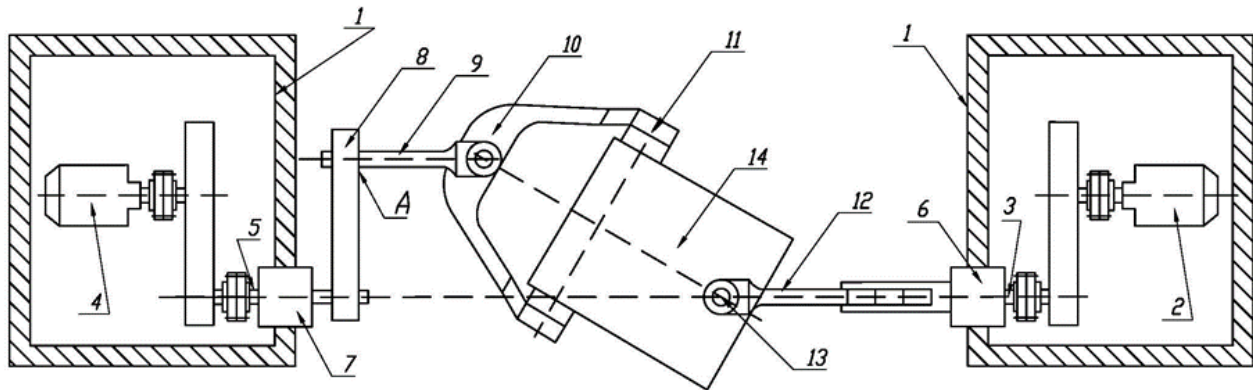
Вид загальний машини нової конструкції для обробки деталей
